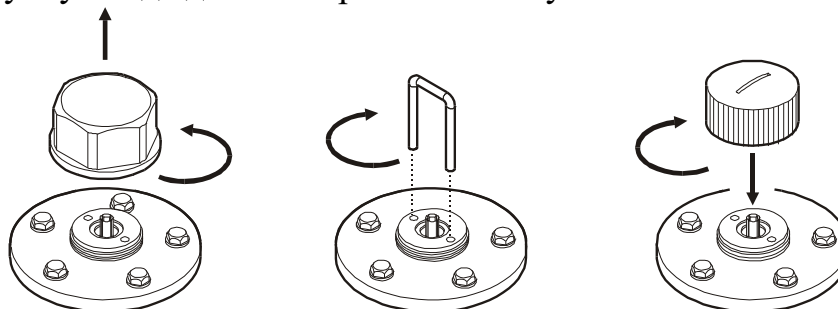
Частичный демонтаж датчика уровня топлива и установка крышки-заглушки
